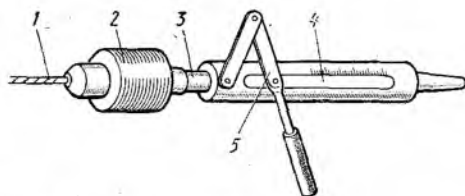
Приспособление для сверления отверстий на заданную глубину
